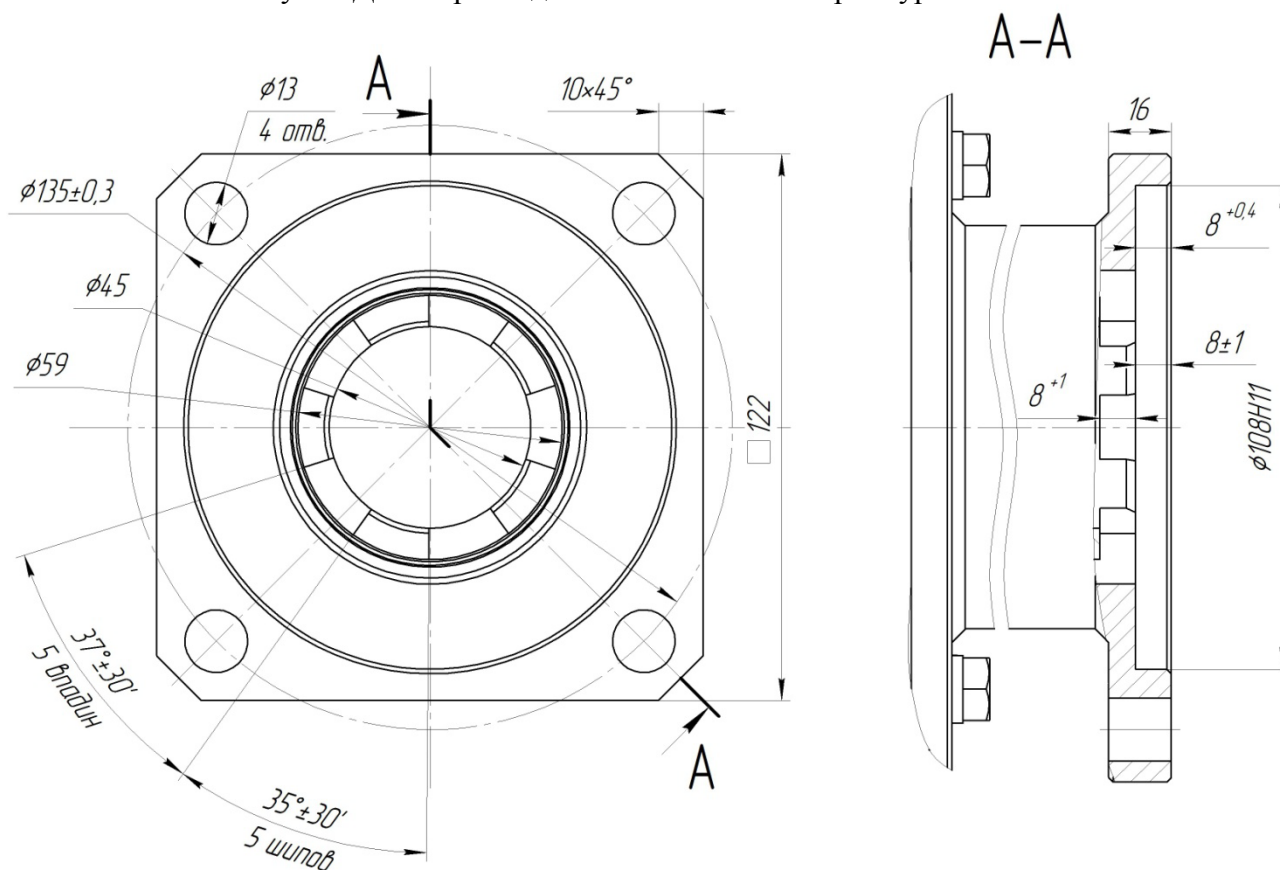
Присоединительное звено к арматуре тип "Б"
